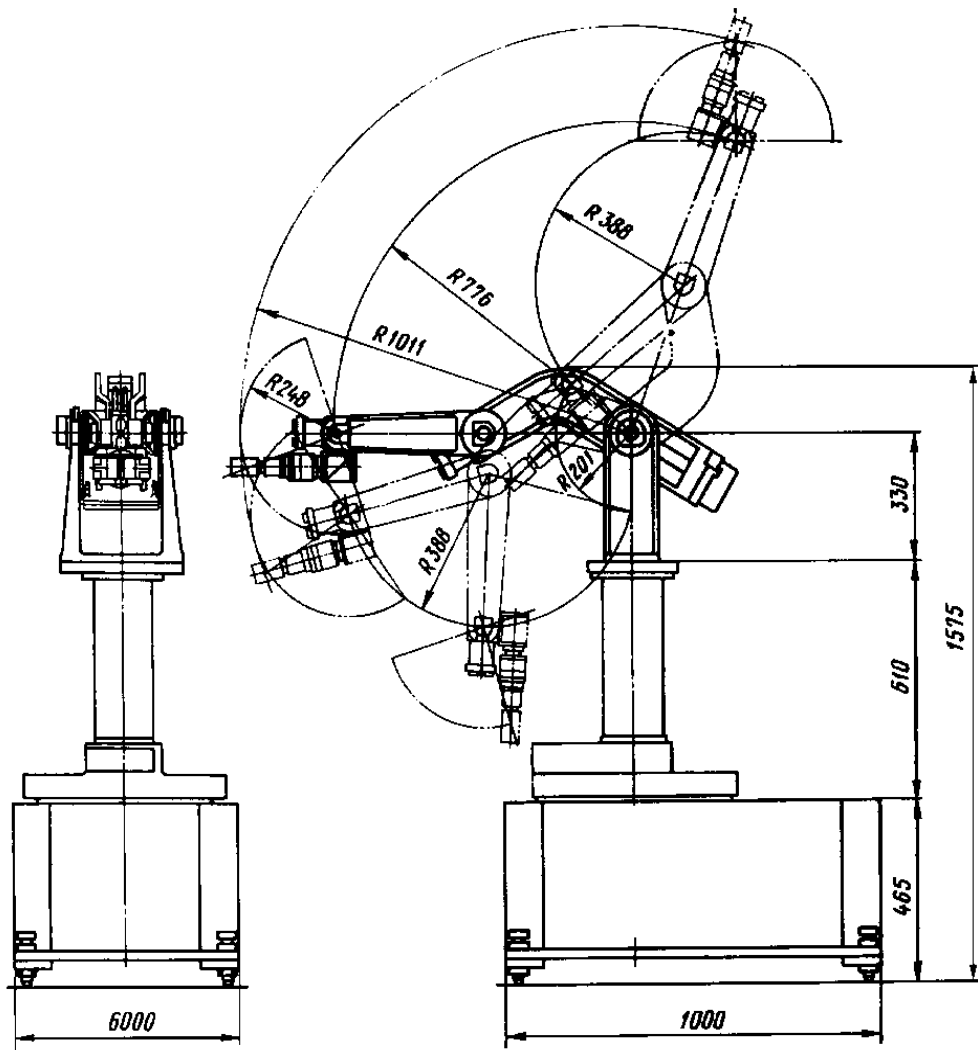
Габаритні розміри і схема руху руки робота KAR-2
